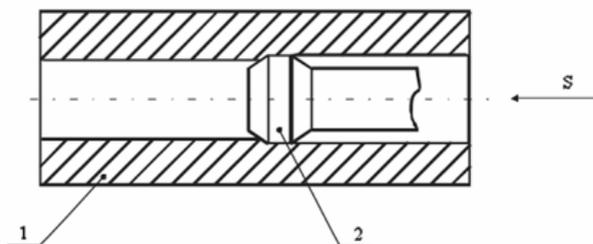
Схема дорнования: 1 – изделие; 2 – дорн;
